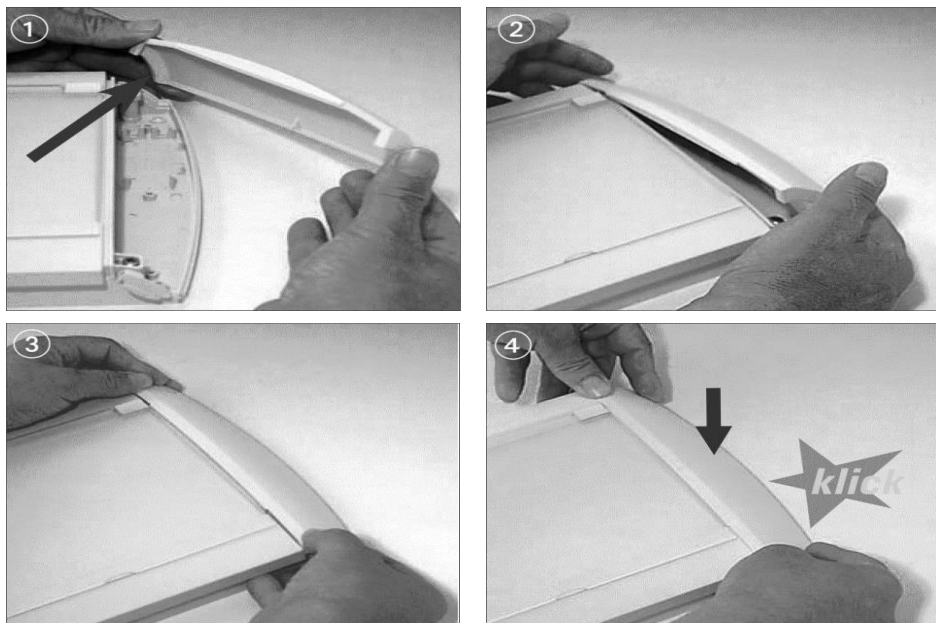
а. Разборка корпуса ЦБ исполнения FP-01-PD.
